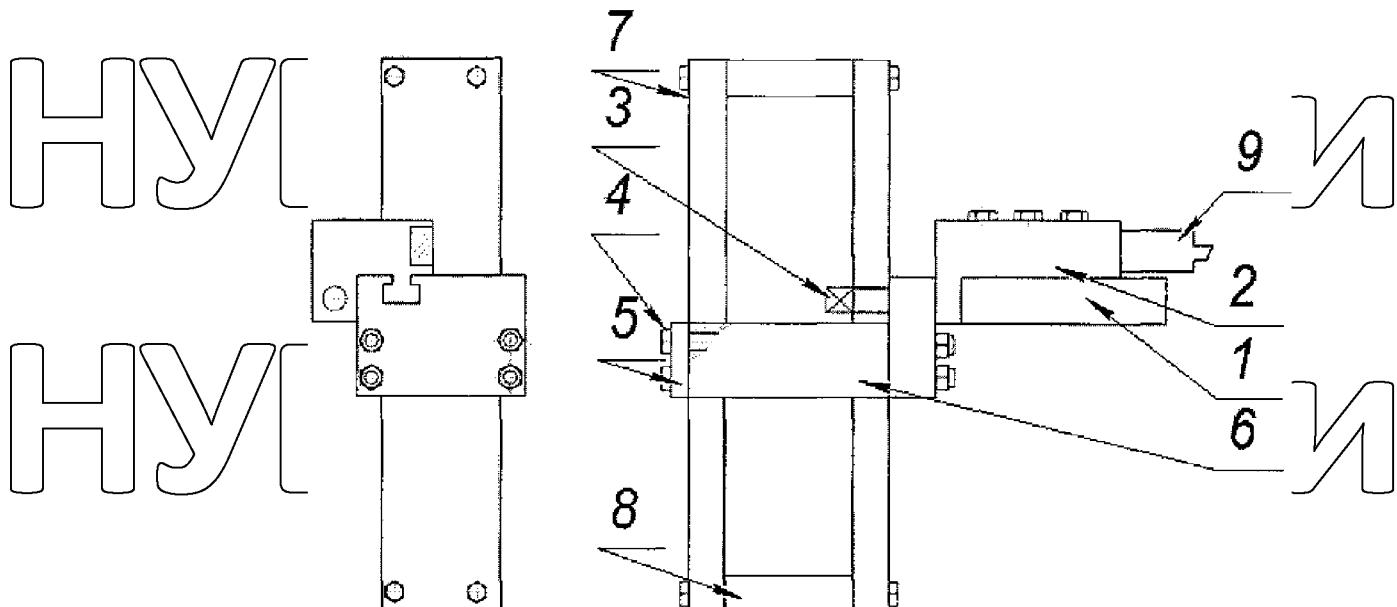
Пристрій для зачистки контактної поверхні
